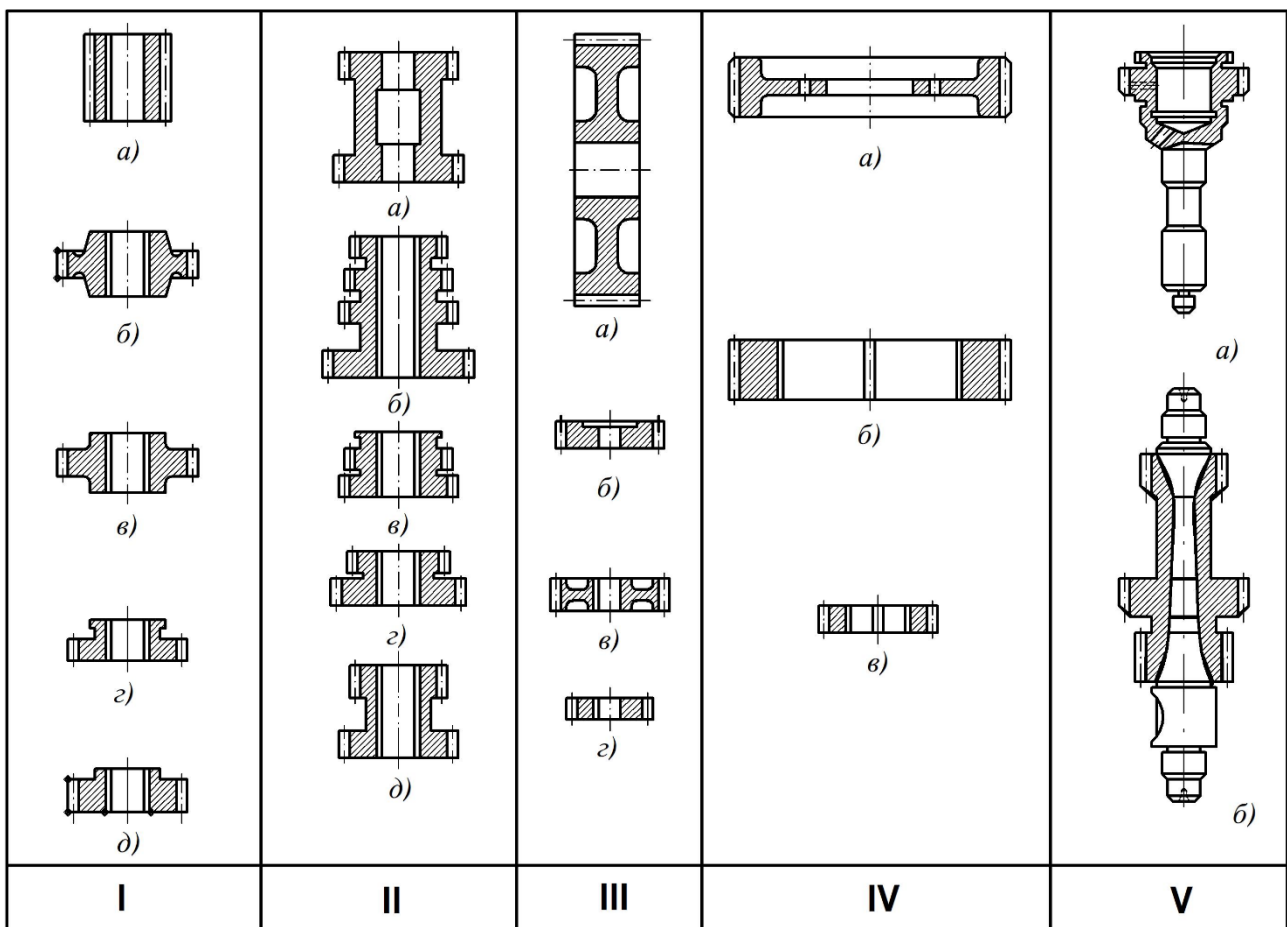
Типові конструкції циліндричних зубчастих коліс
